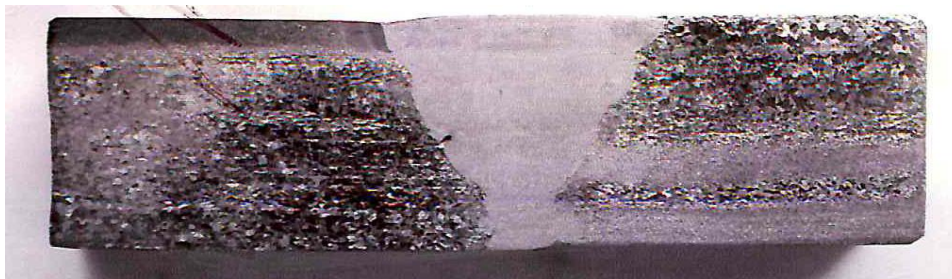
Вид сварного шва в соединении кованое железо + кованое железо
